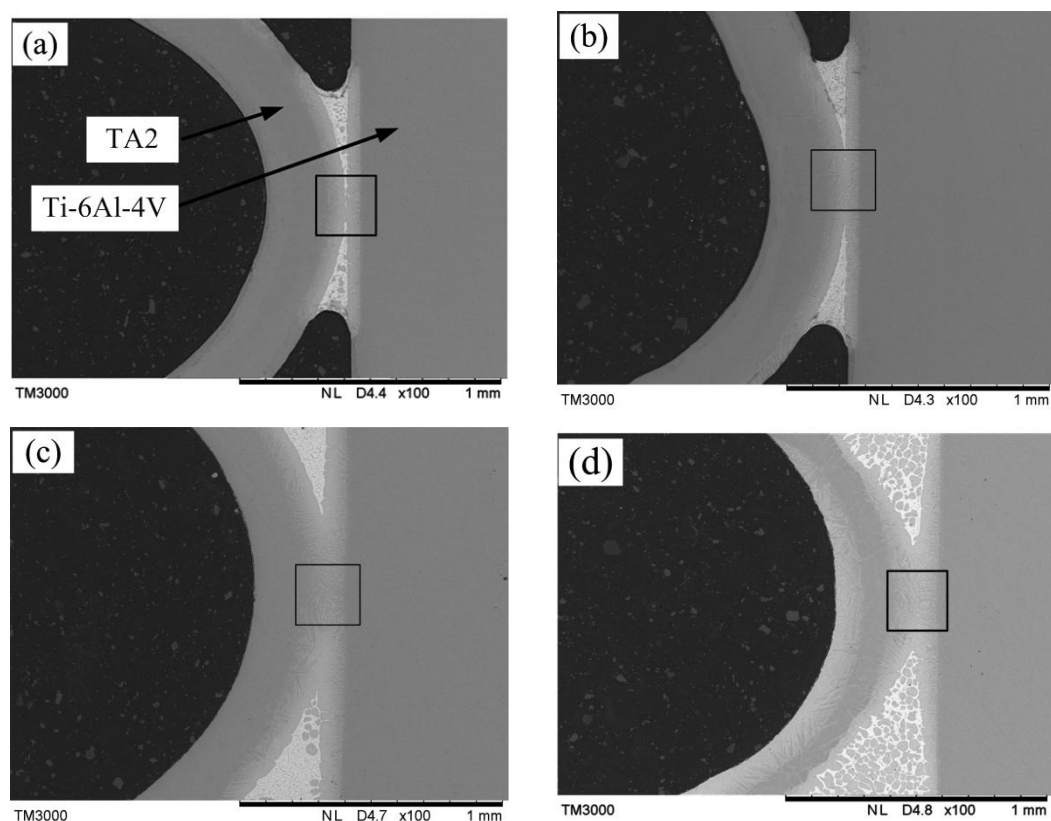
870°C 下不同钎焊时间钎焊接头宏观形貌
